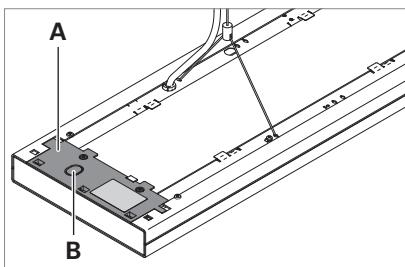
Copertura dell'apparecchio d'illuminazione a sospensione LAVIGO.
